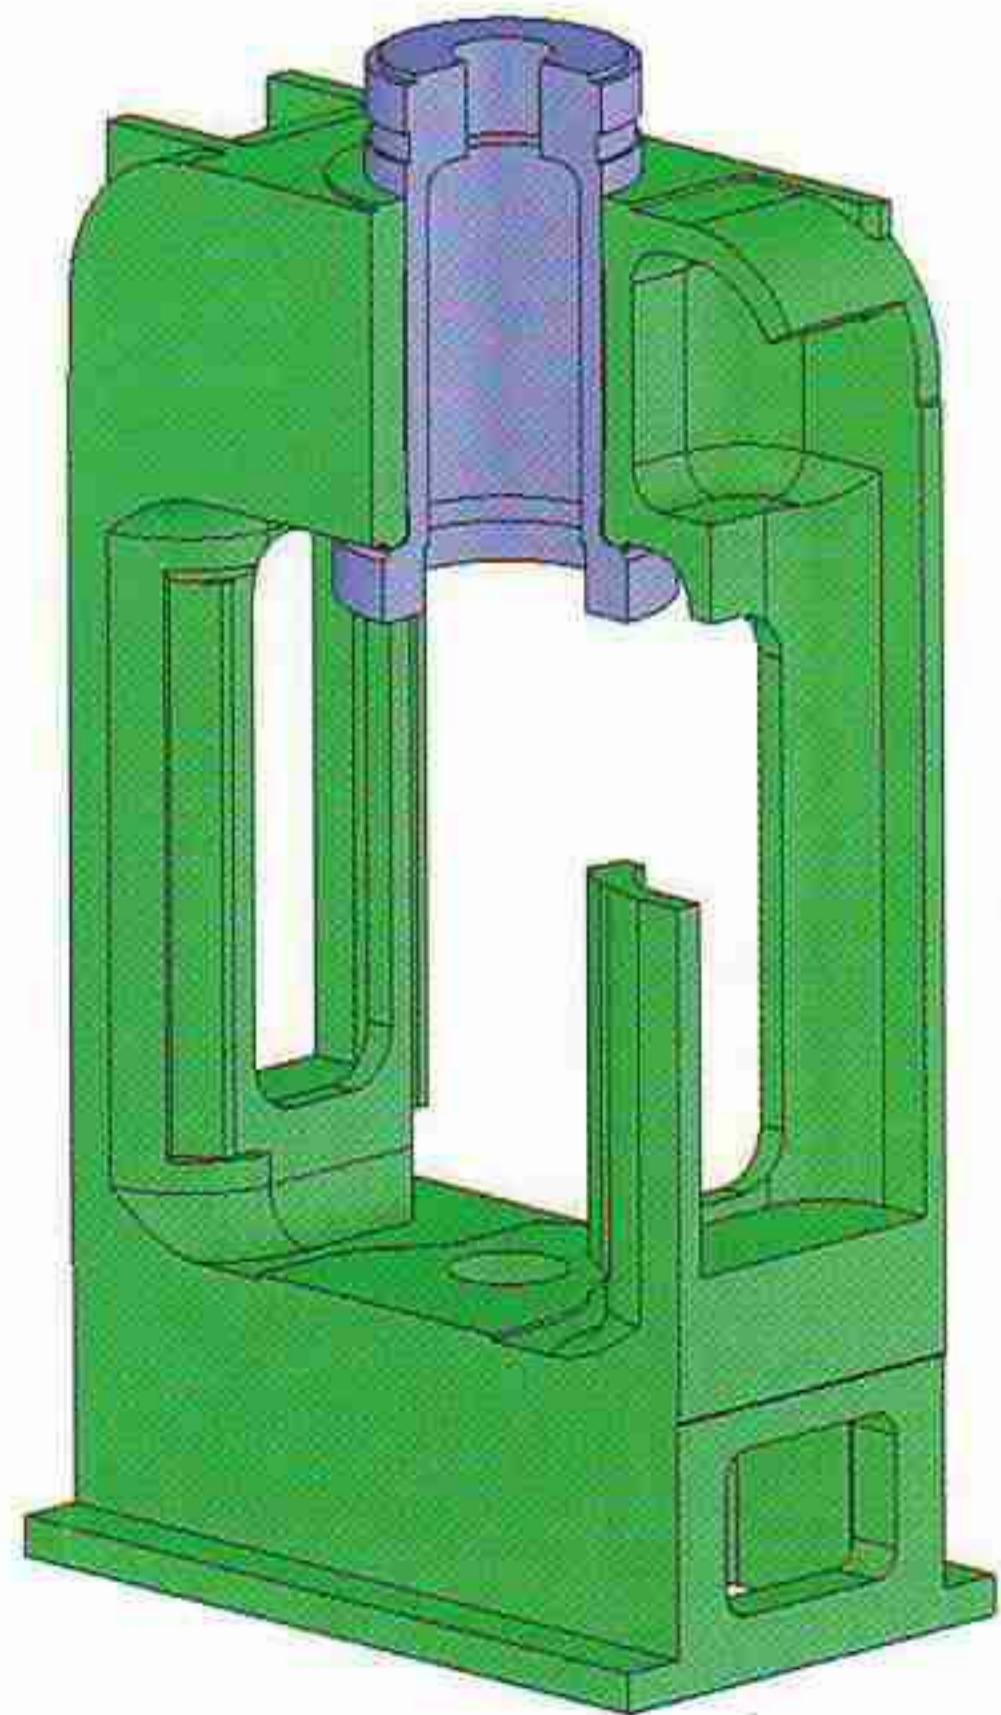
Станина пресса мод. ПА8340 в сборе с цилиндром
